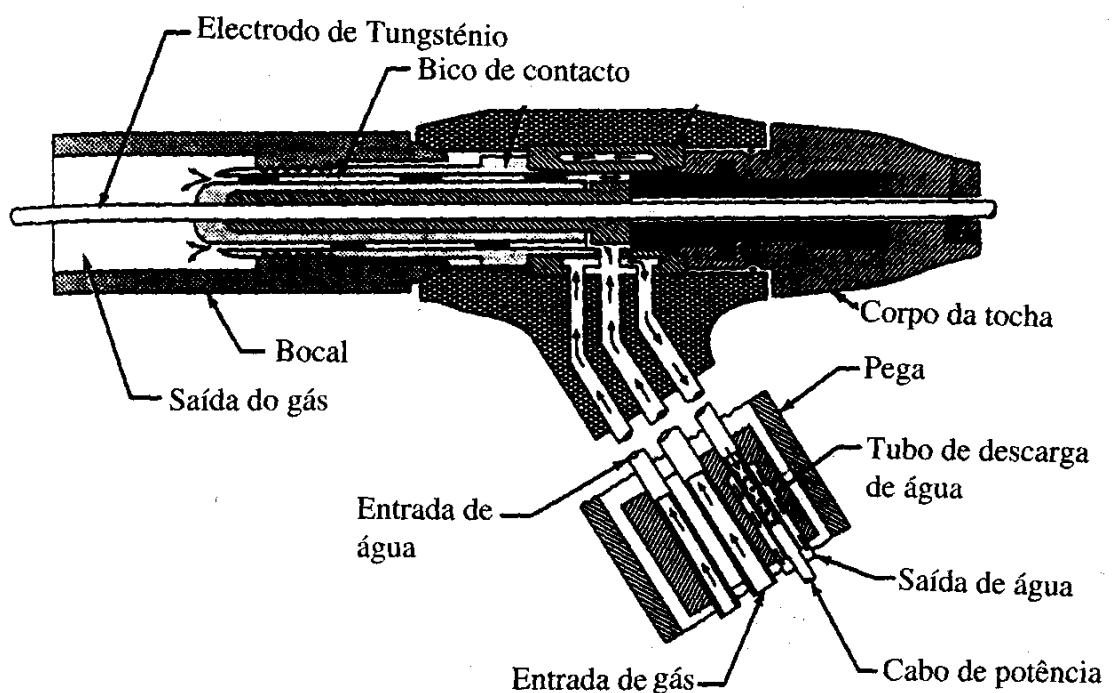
Tocha de soldadura TIG [2].
